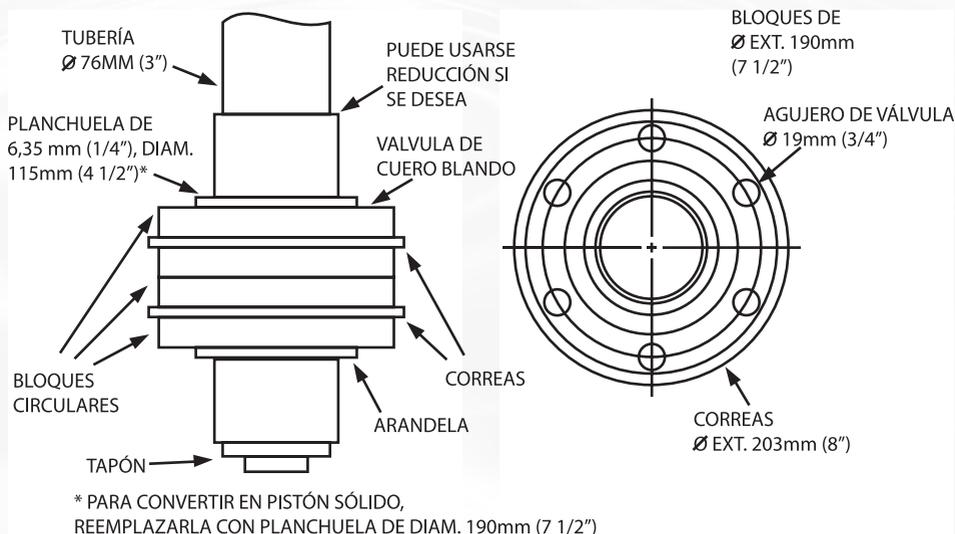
Dibujo del pistón con válvula mostrado en la Figura 4 y dimensionado para entubamiento 0 int. 203 mm. (8").
